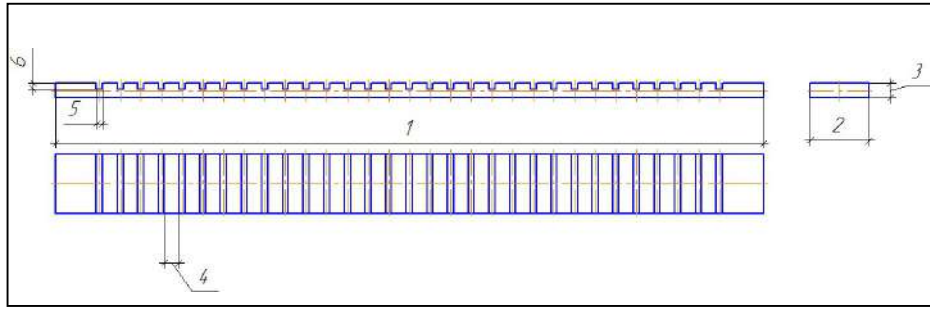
Ескіз пластини та розміри контрольовані під час її технологічного процесу виготовлення
